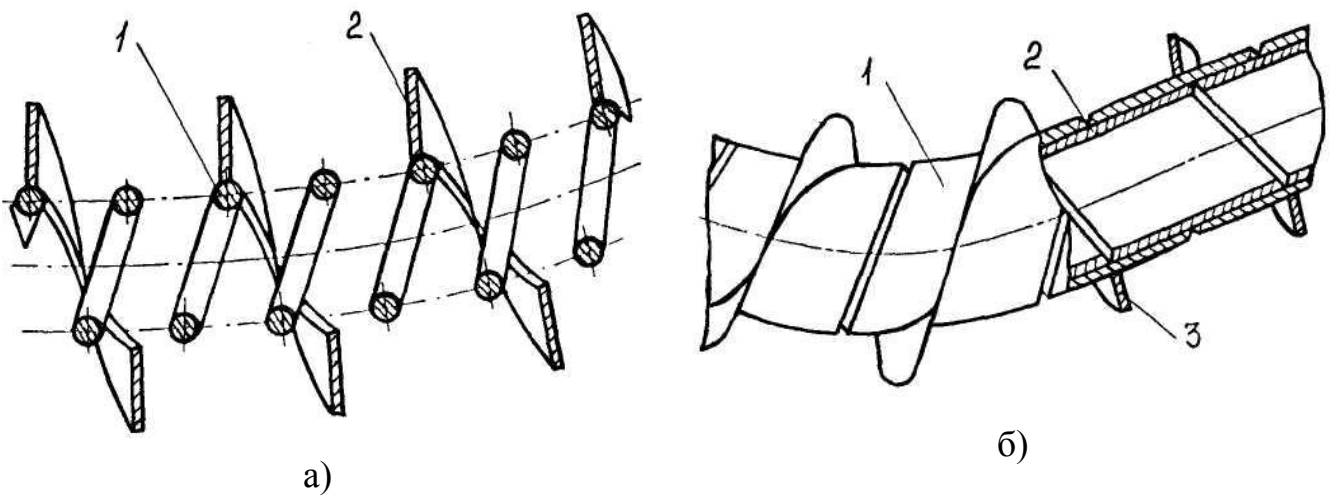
Робочі органи МГА з пружинними гнучкими валами
